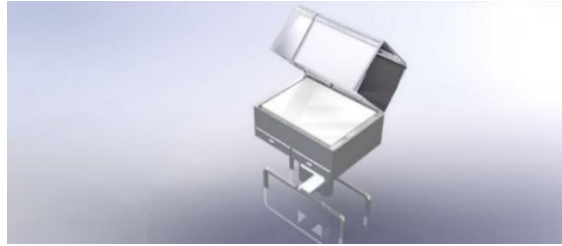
Diseño preliminar cuna con mecanismo de engranajes.
